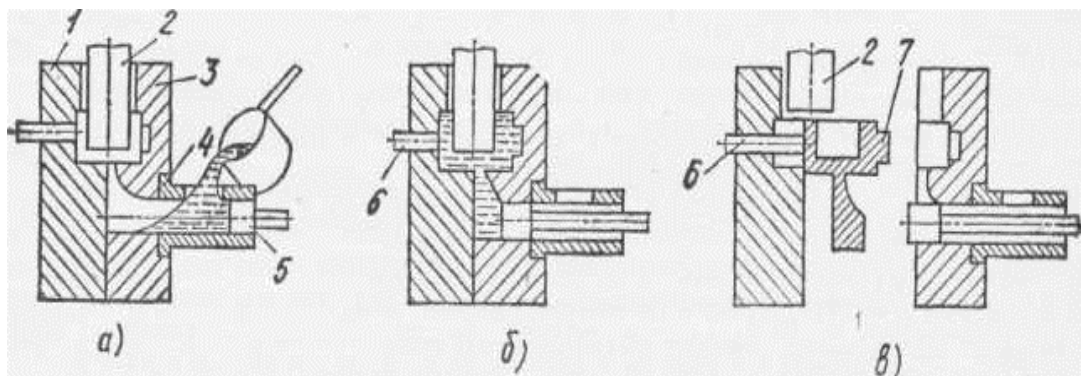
26. Схема процесса изготовления отливок на машинах с горизонтально холодной камерой прессования
